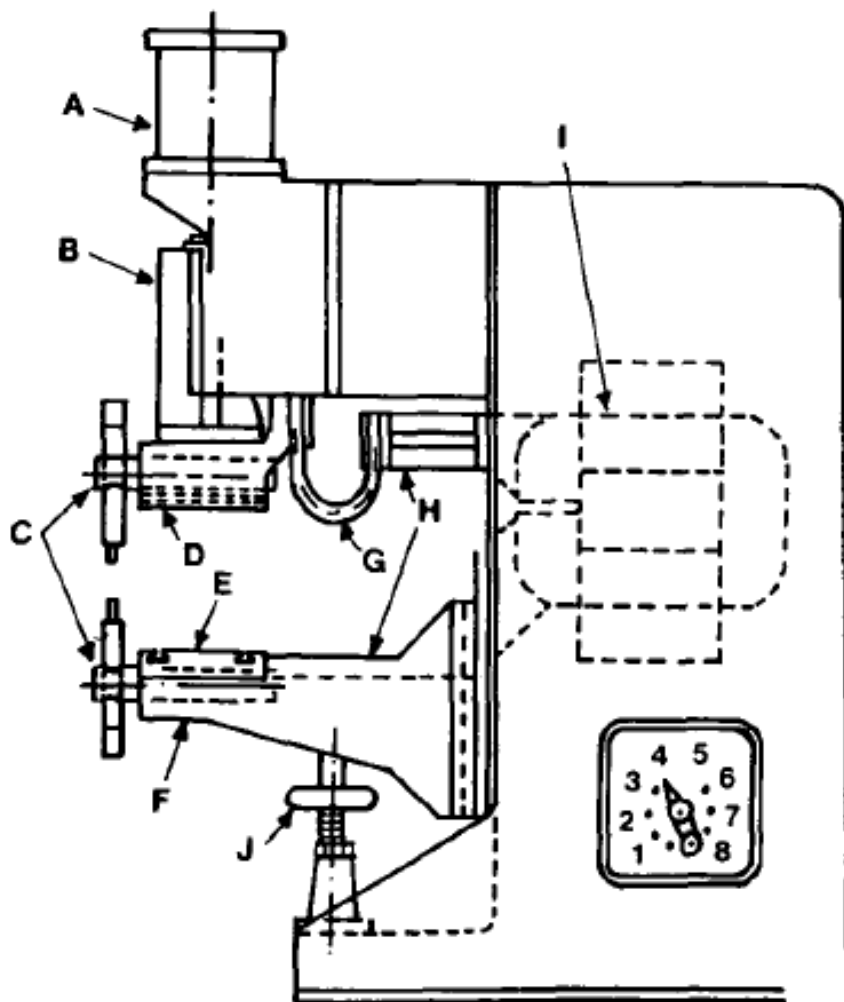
Máquina de solda por resistência, tanto por ponto como por ressalto. A- cilindro hidráulico ou pneumático; B- cabeçote de solda; C- eletrodos com seus suportes; D- mesa superior; E- mesa inferior; F- chapa inferior de reforço; G- contatos flexíveis; H- terminais de contato superior e inferior; I- transformador secundário; J- suporte da chapa de reforço e macaco de parafuso.
